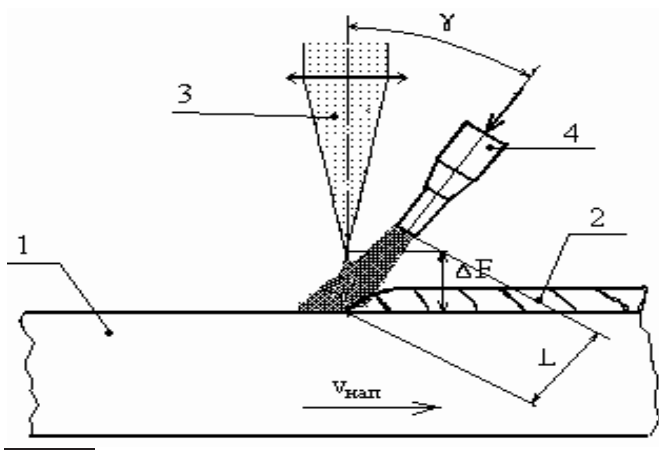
Схема лазерной наплавки с подачей порошка вслед движению луча. 1 - образец, 2 - наплавленный валик, 3 - лазерное излучение; 4 - сопло подачи порошка
